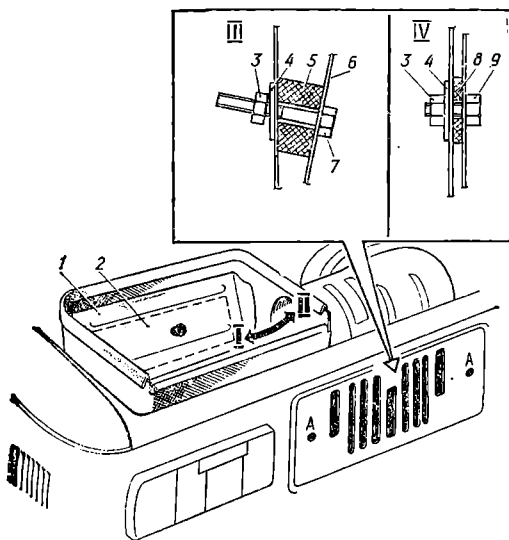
Воздуховод охлаждения двигателя и крепление заднего номерного знака:
